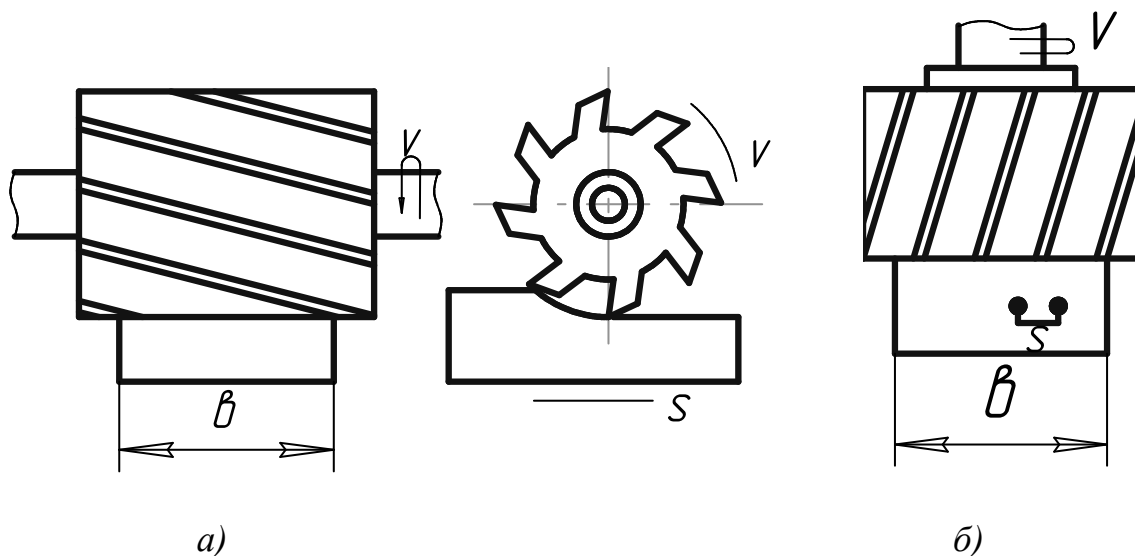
Схеми фрезерування площин фрезною:
